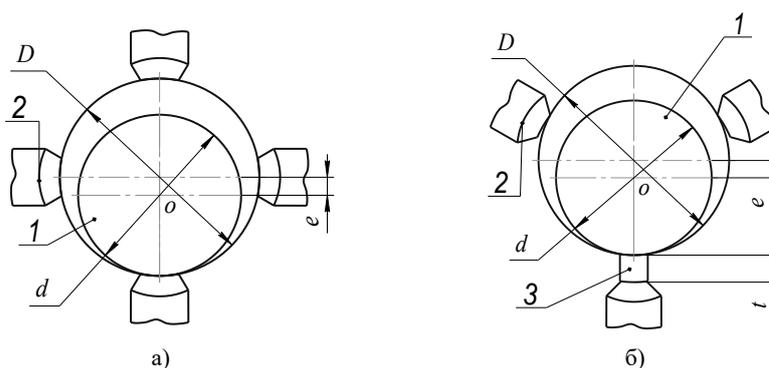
Схема эксцентричной установки заготовки на токарном станке:
